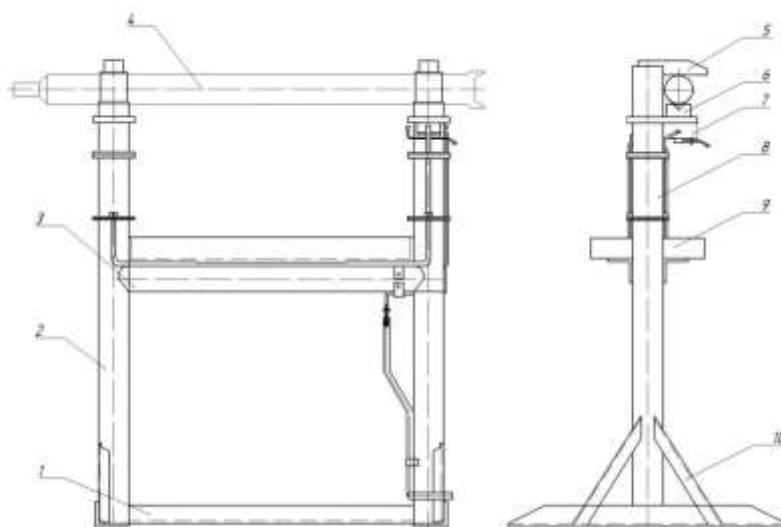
Стенд модель 3025: 1 – поперечка; 2 – стійка; 3 – поперечка; 4 – виріб; 5 – притиск; 6 – призма; 7 – пневматичний кран; 8 – пневмоциліндр; 9 – піддон
